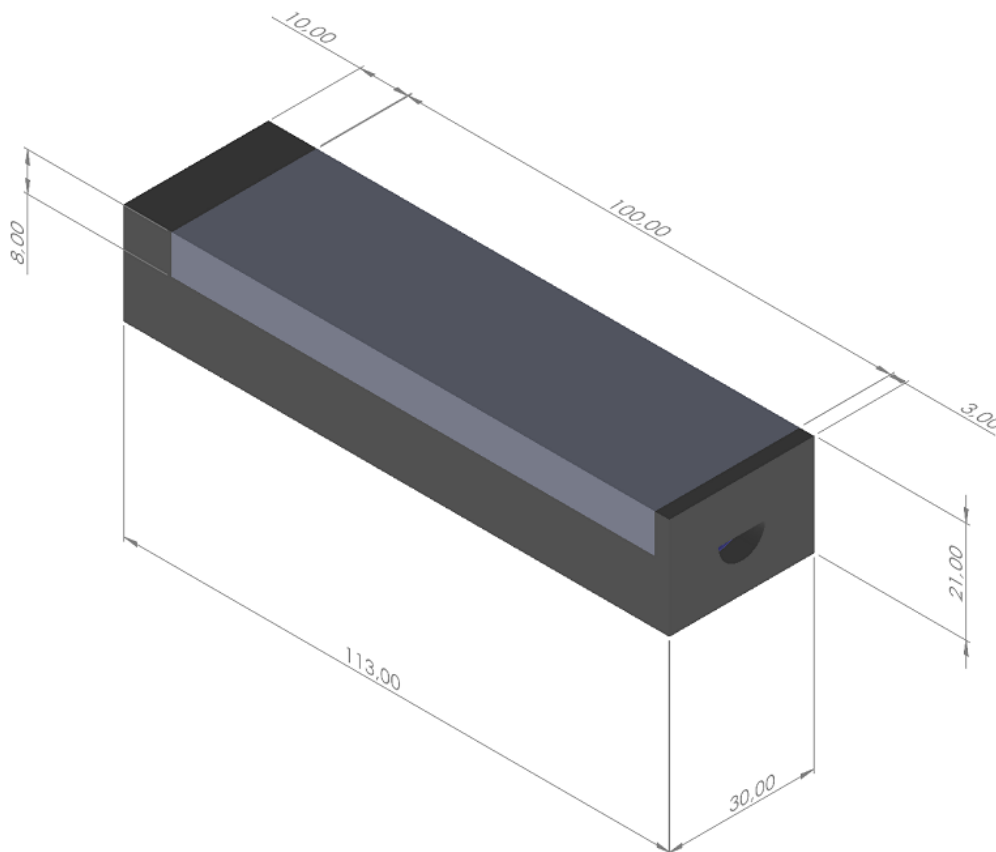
Stampo interno assemblato con le rispettive quote in millimetri
